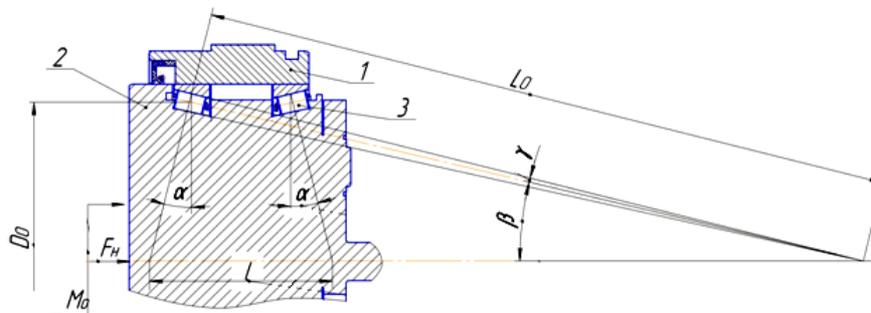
Вариант компоновки совмещенных опор качения планетарно-цевочного редуктора типа ПЦР 3-36(6): 1 – корпус; 2 – водило; 3 – радиально-упорная совмещенная опора качения; α – угол контакта конического ролика; M_o – опрокидывающий момент; F_n – внешняя осевая сила; L – расстояние между точками приложения опорных реакций; L_o – длина среднего конусного расстояния ролика; D_o – диаметр центров комплекта роликов; β – номинальный угол контакта ролика; γ – угол конусности ролика
